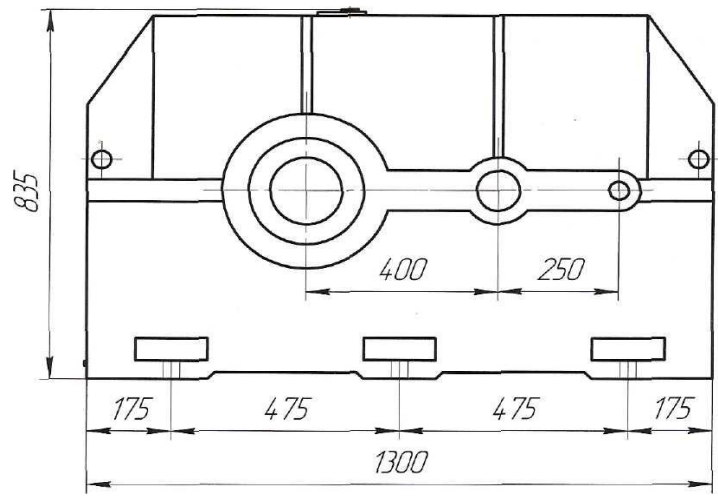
Ескіз редуктора типу Ц2У-400
